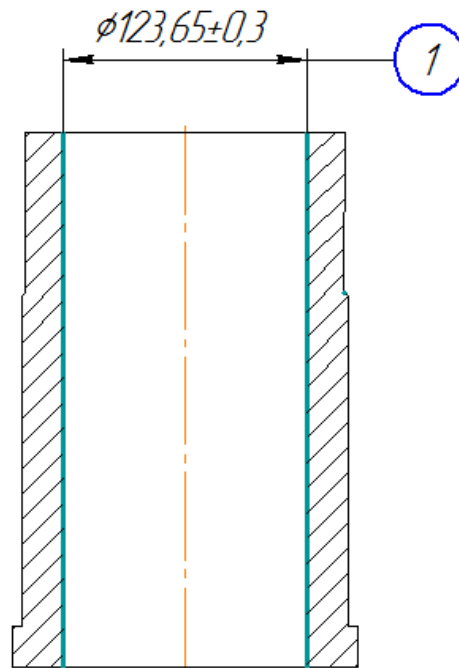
Ескіз обробки заготовки на операції 015
